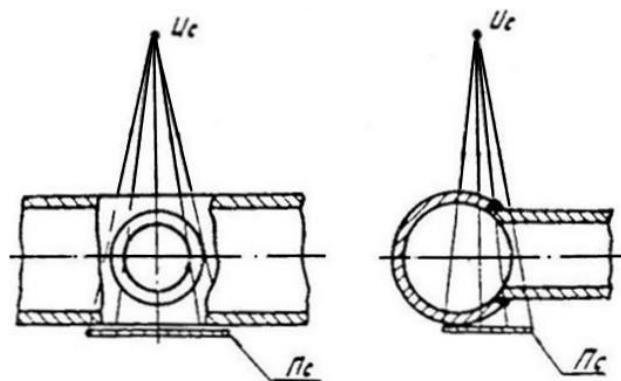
Схема фронтального просвечивания через две стенки за одну установку для соединения врезок
